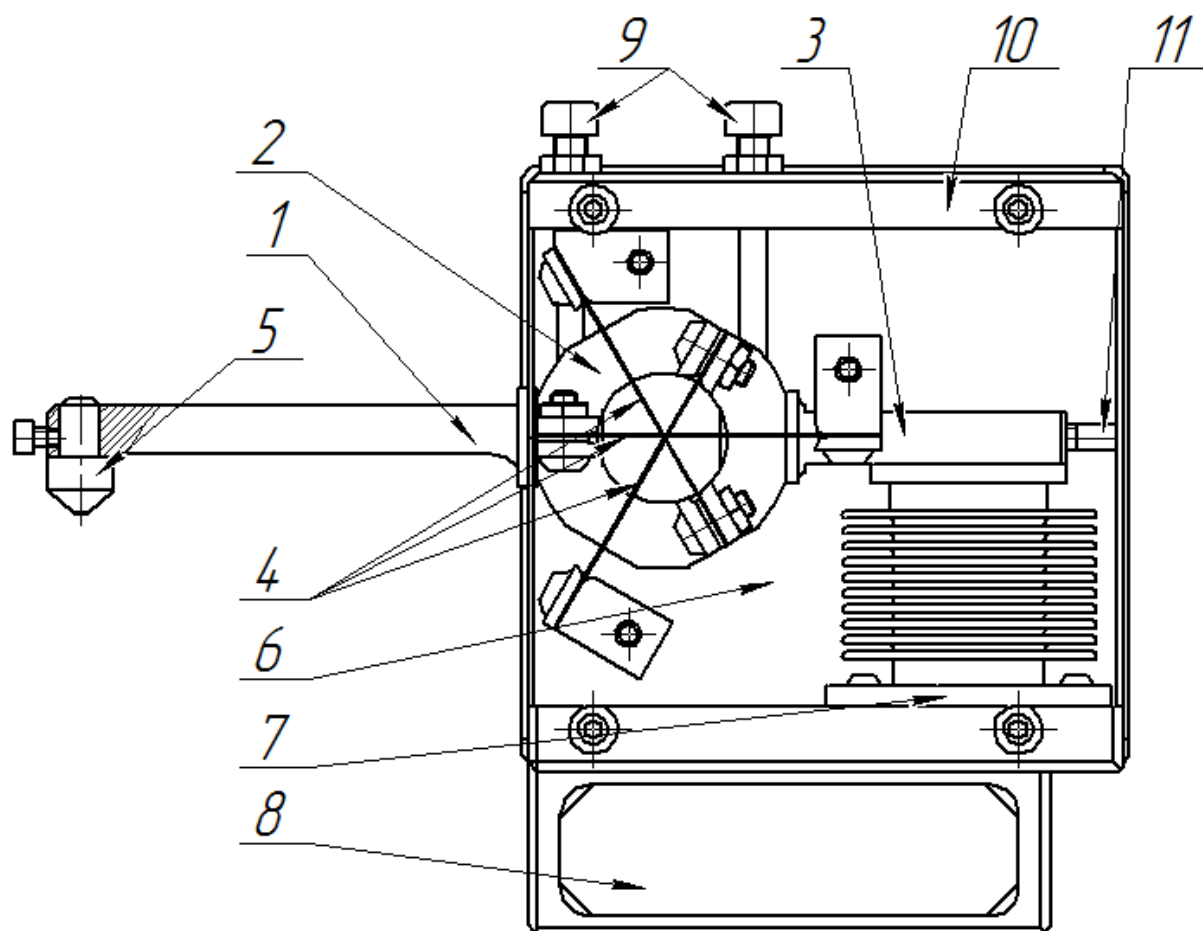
Эскиз пневматической оправки с пружинами для внутреннего выглаживания
